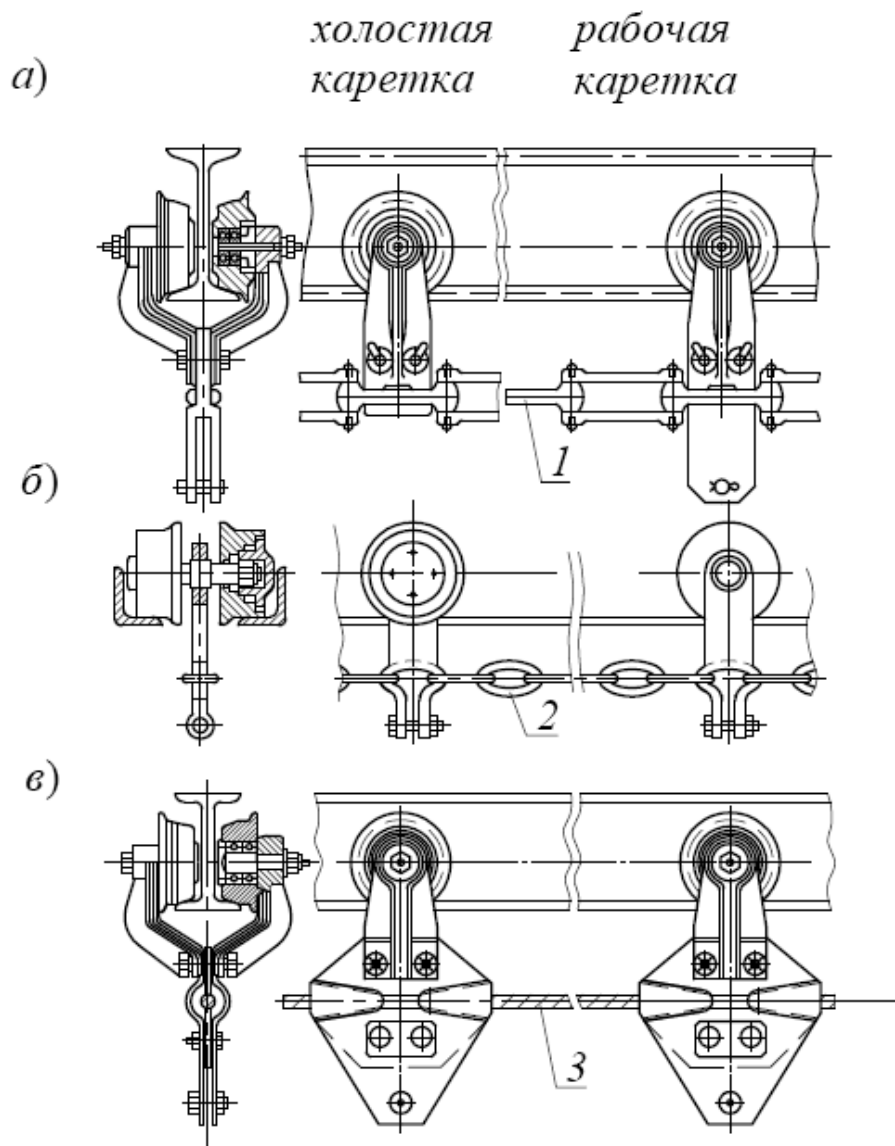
Крепление кареток грузонесущих конвейеров к тяговым органам: *а* – штампованными разборными цепями; *б* – сварными цепями; *в* – канатами
